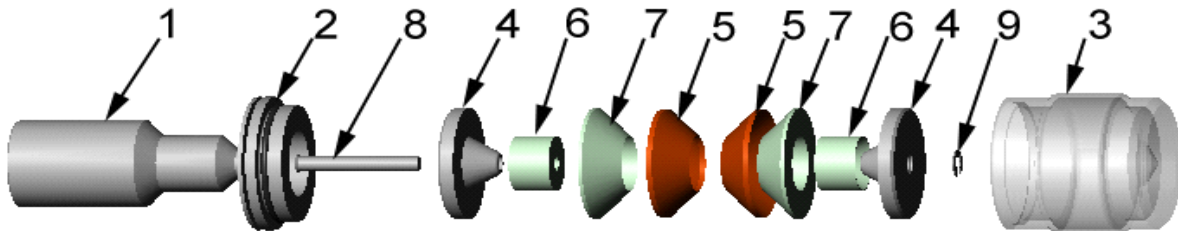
Vue éclatée, dimensions 2,500 po (6,35 cm) et 3,000 po (7,62 cm)
